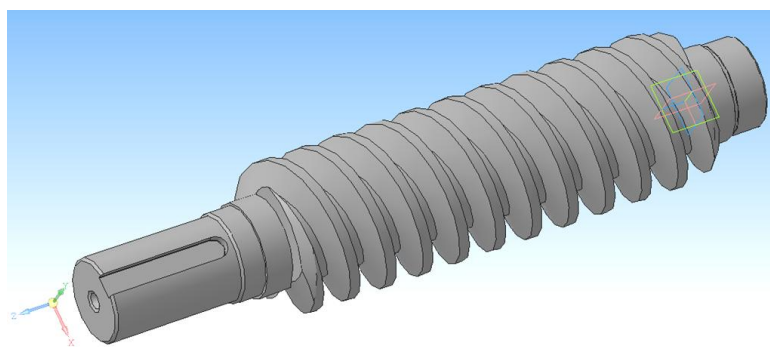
3D-модель детали «Шлицевой вал»
